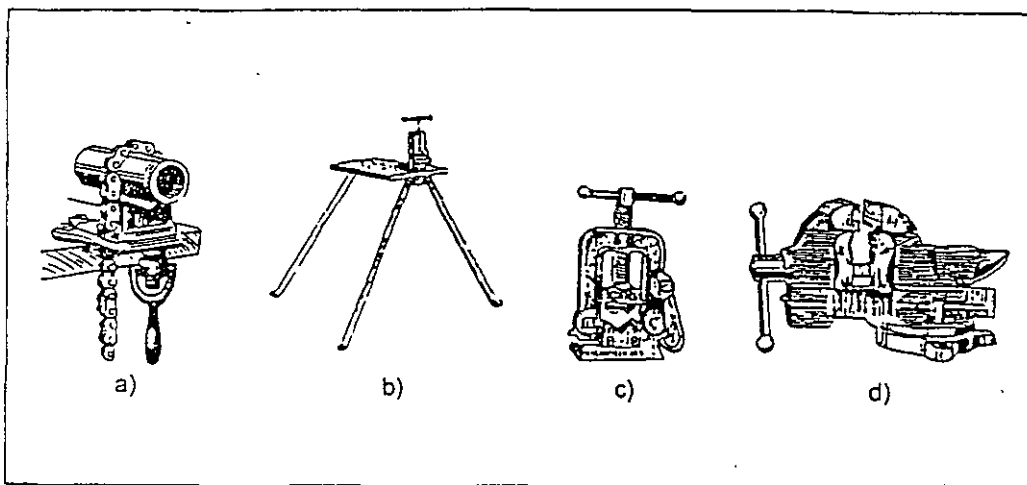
Herramientas de taller: a) Tornillo de banco de cadena. b) Caballete para tornillo de banco. c) Tornillo de banco de mordaza. d) Tornillo de banco de quijadas.
